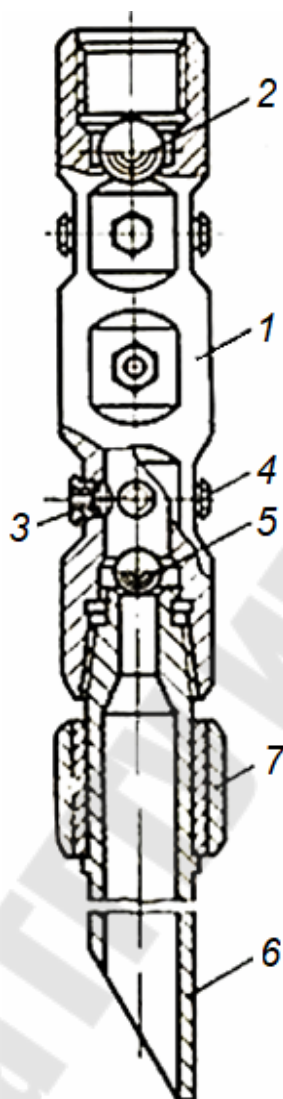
Аппарат для пескоструйной перфорации АП-6М: 1 – корпус; 2 – шар опрессовочного клапана; 3 – узел насадки; 4 – заглушка; 5 – шар клапана; 6 – хвостовик; 7 – центратор
